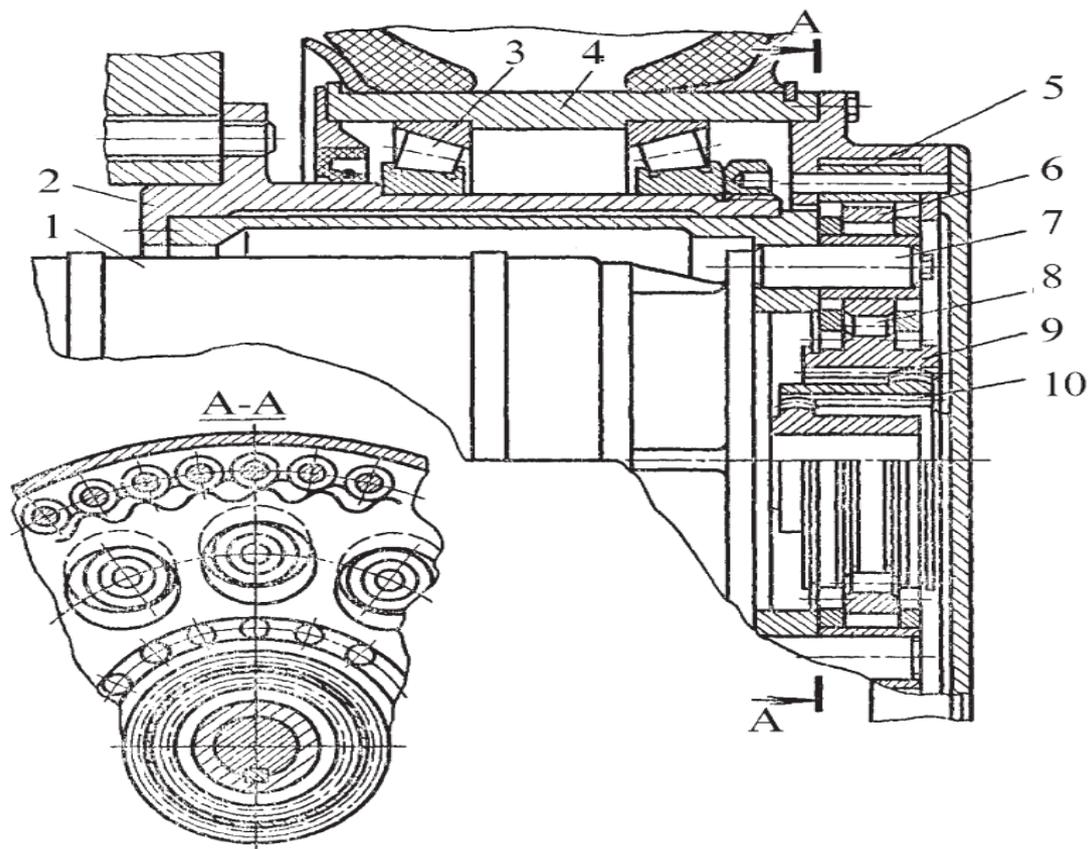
Конструкция мотор-колеса на основе планетарно-цевочного редуктора
